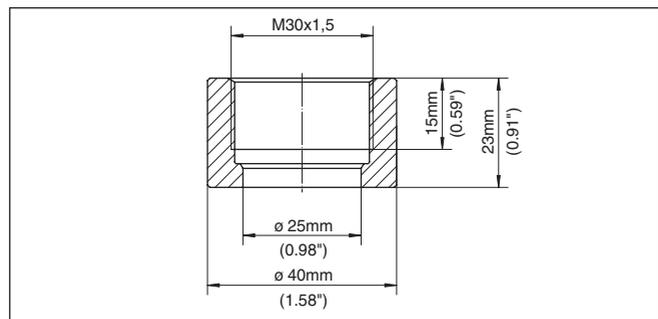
Medidas luva para soldagem M30 x 1,5 - VEGABAR 82
